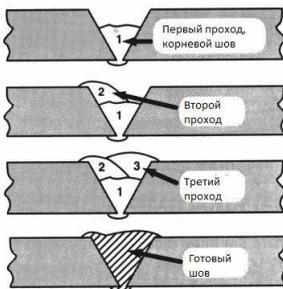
Многопроходная сварка стыковых соединений
